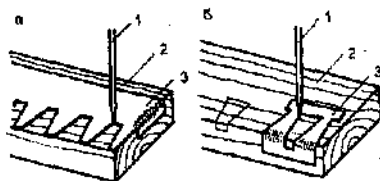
Шаблоны: а — для разметки шипов; б — для разметки в «ласточкин хвост»; 1 — чертилка; 2 — заготовка; 3 — шаблон
